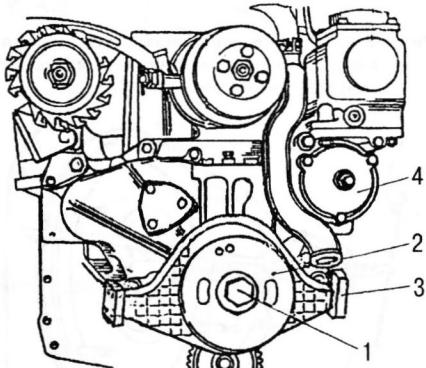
Снятие передней опоры двигателя, шкива коленчатого вала и лючка: 1 – болт; 2 – шкив коленчатого вала; 3 – передняя опора; 4 – крышка лючка
